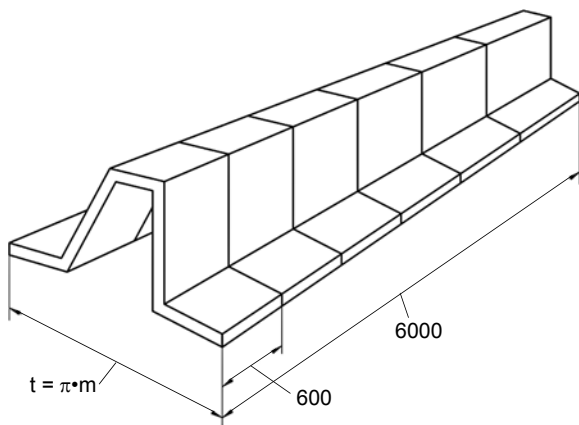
Схема гнутого зубчатого сегмента, изготовленного из листового проката
